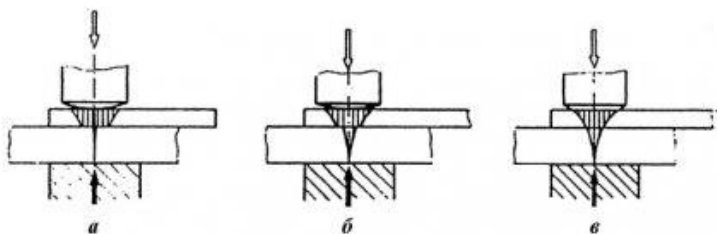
Распространение ультразвуковых колебаний при сваривании: а - начало сваривания; б - процесс сварки; в - окончание процесса [5].
